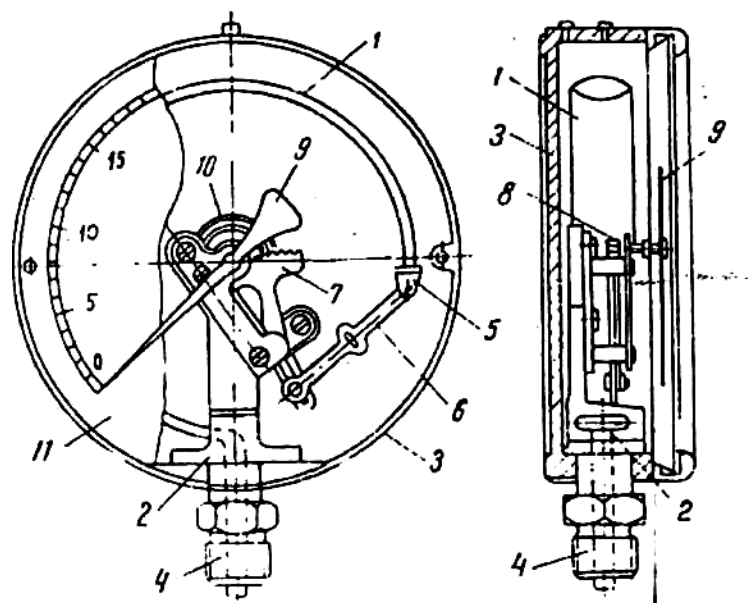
Показывающий манометр с одновитковой трубчатой пружиной.
